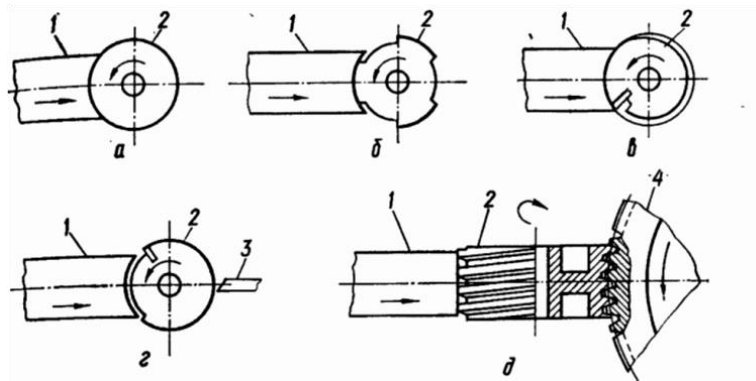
Принципова схема роботи електроконтактної обробки тіл обертання
